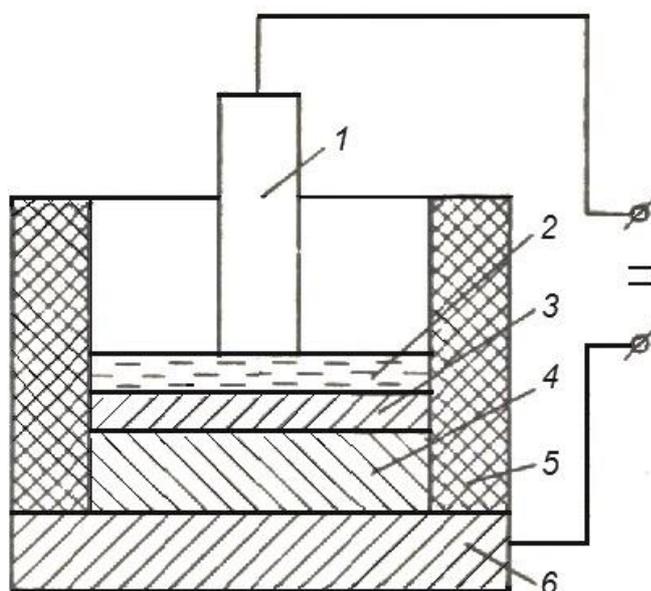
Схема наплавки зубьев ковша экскаватора:
